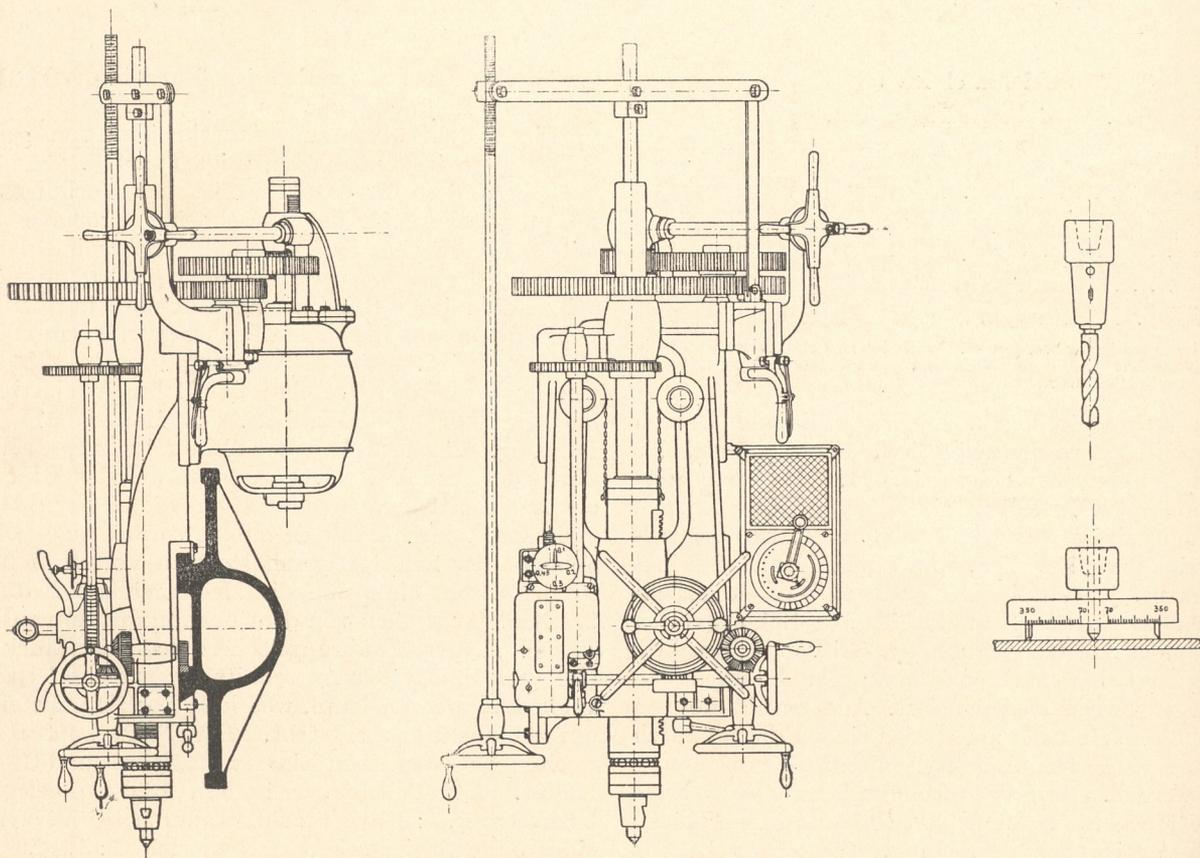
Bohrkörper mit Körnerstange für Messerbohrer.
